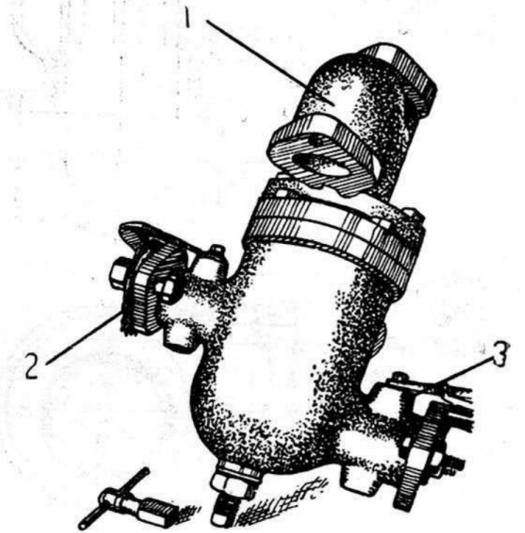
Общий вид смесителей КОЛОН-I. 1—колесо крепления смесителя с карбюратором и двигателем; 2—патрубок газа; 3—патрубок воздуха
